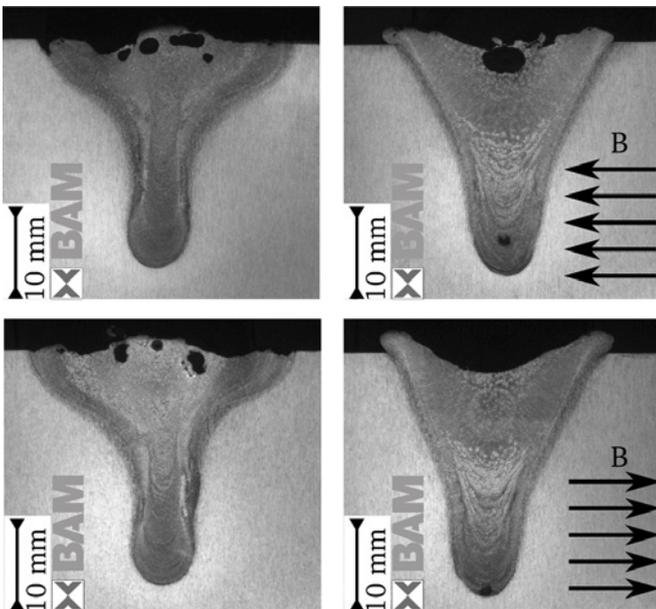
Querschliffe an Schweißungen mit gedrehter Polarisation des magnetischen Feldes, Laserleistung 16 kW, Vorschubgeschwindigkeit 0,5 m/min (links: Referenzfall $B=0$ T, rechts magnetisch beeinflusste Schweißung $B=0,5$ T)
